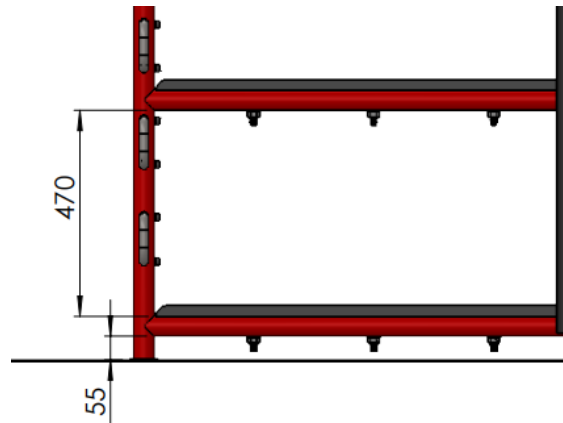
Dimensiones para soldar el elemento 2.6.1/3.9.1/4.7.1 (en los planos 2.6.1). Fuente: Elaboración propia
